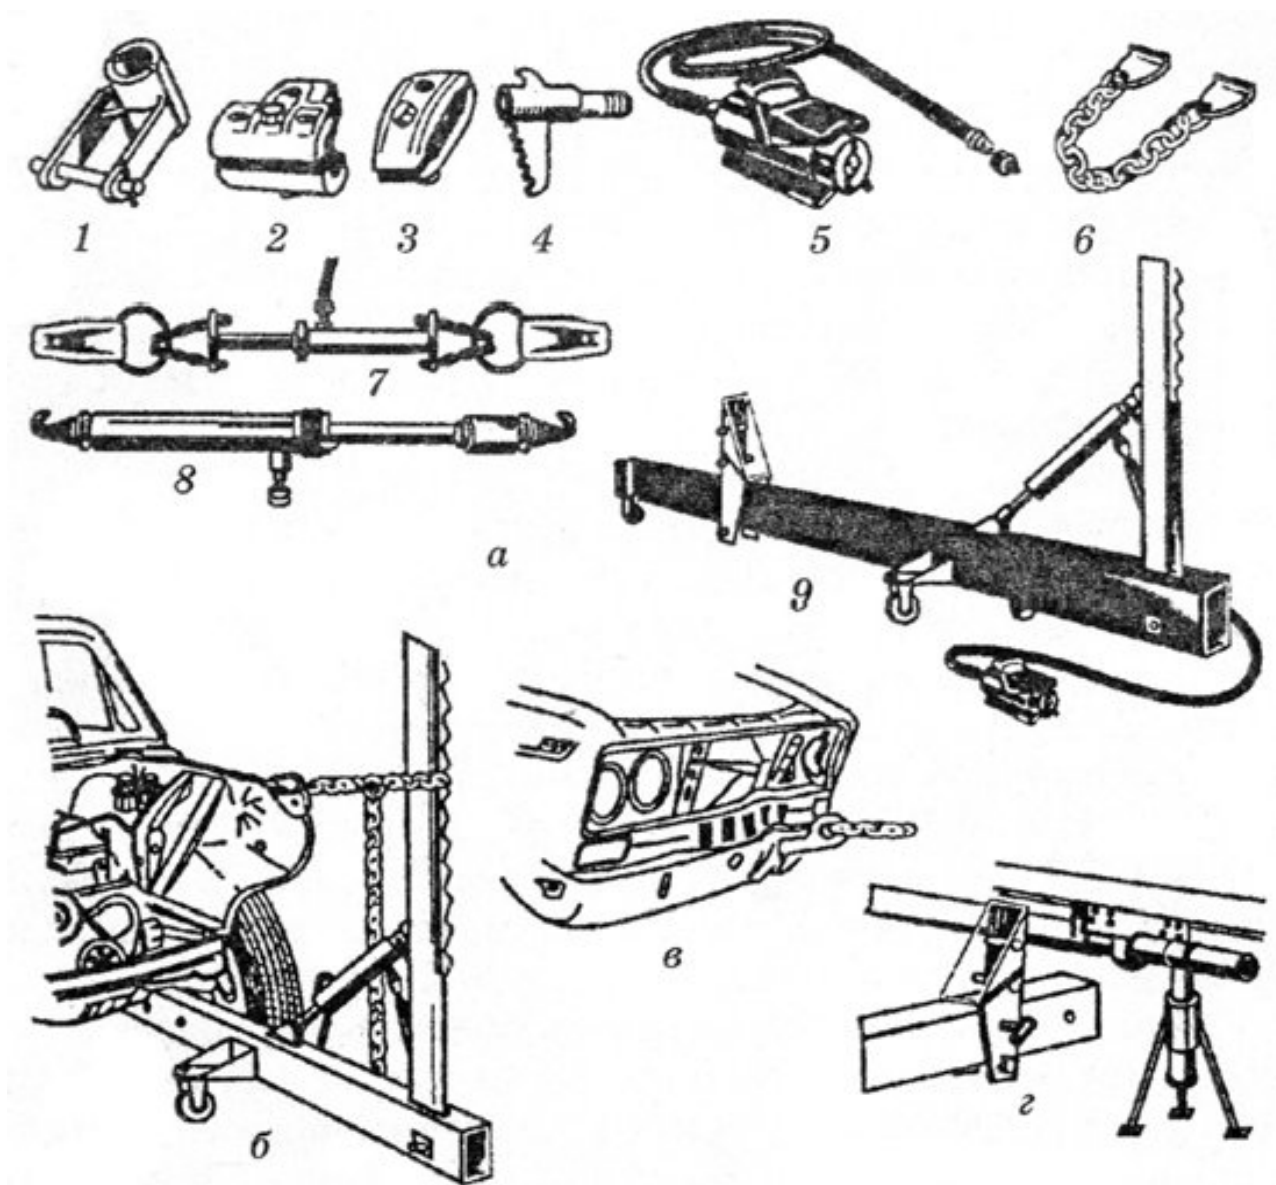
Приспособления для выполнения правки деформированного участка кузова:
